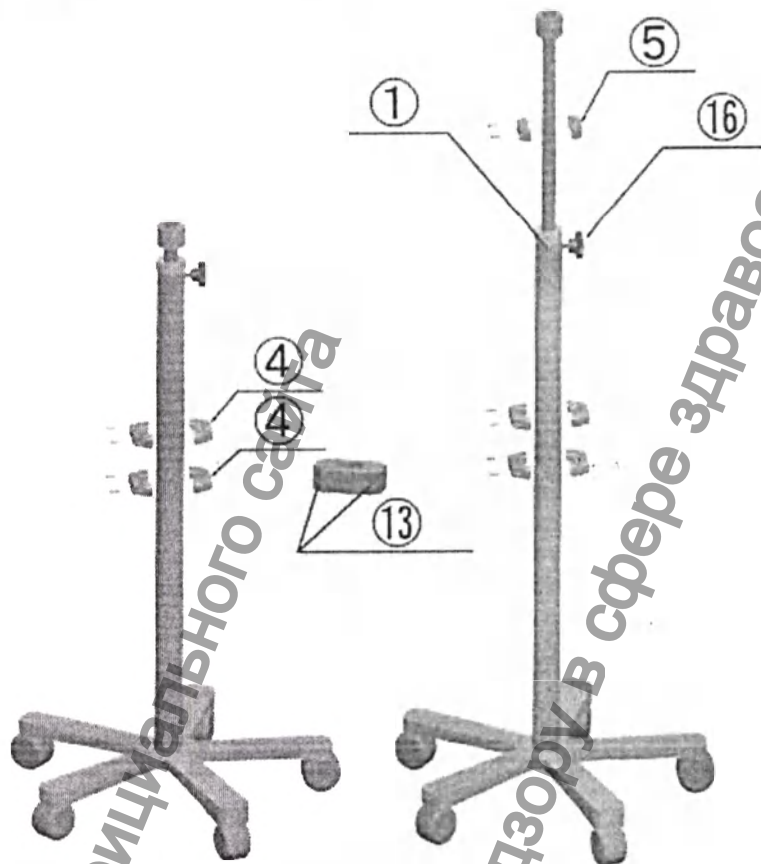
Сборка медицинской стойки Endostand Шаг 2
